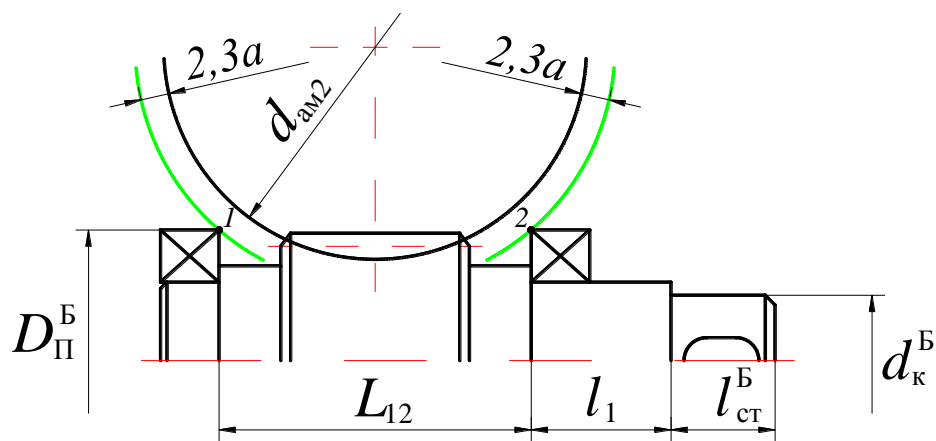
Схема для определения расстояния между подшипниками червячного вала
